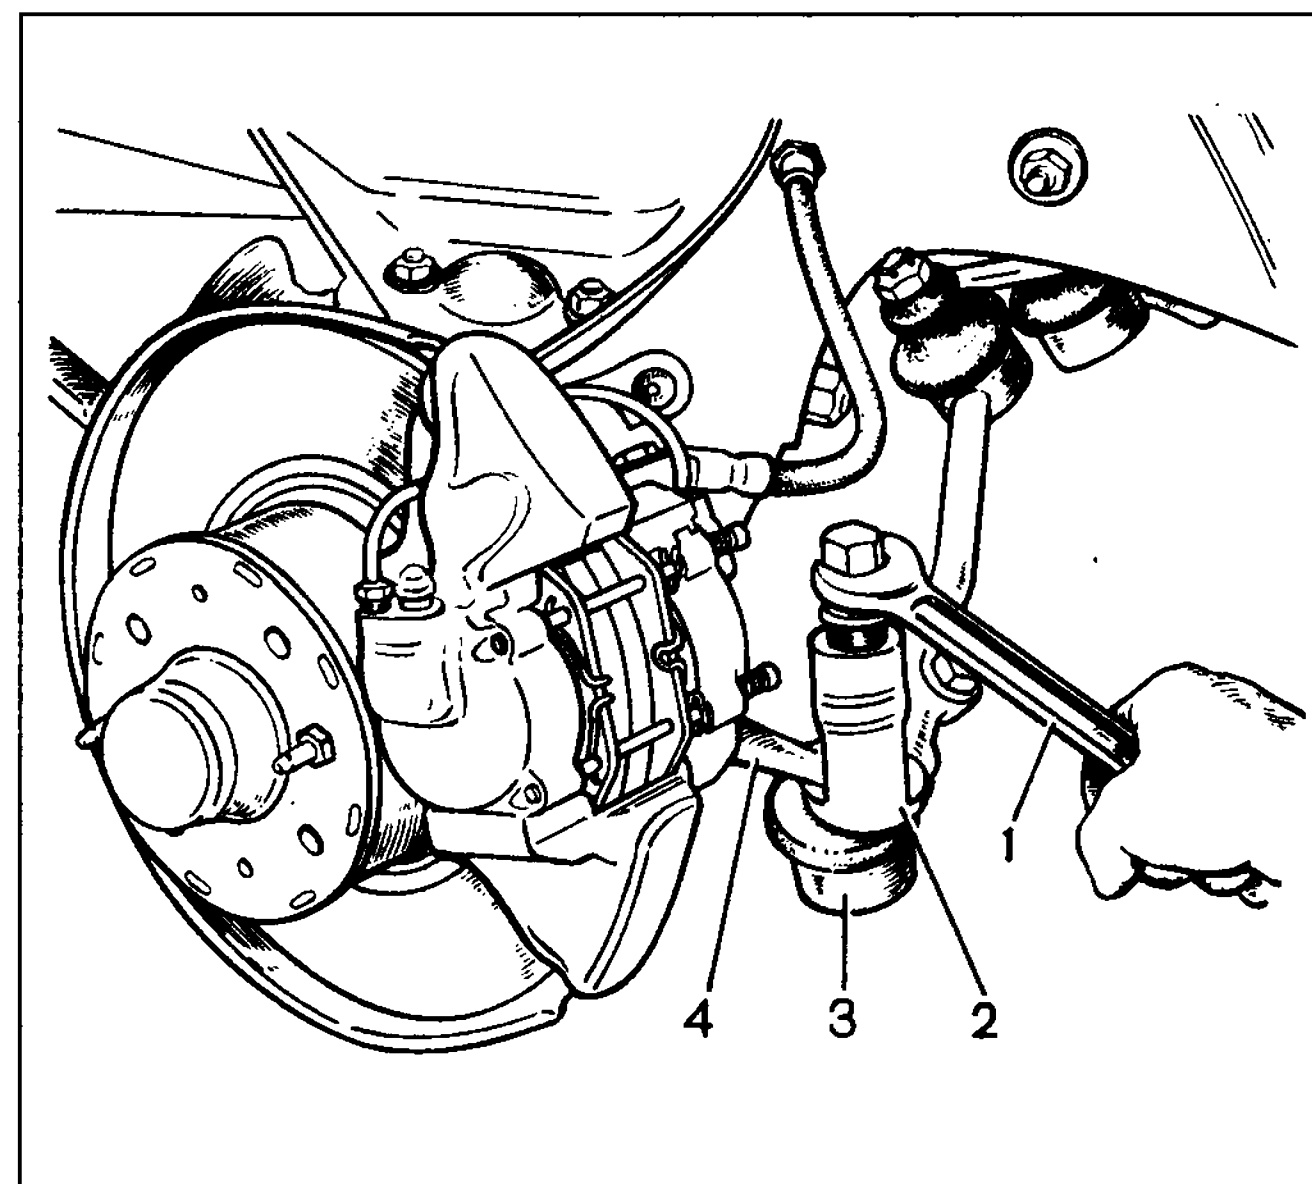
Снятие шаровых пальцев тяг рулевой трапеции: 1-ключ гаечный; 2-съемник А.47052; 3-шаровой шарнир; 4-рычаг поворотного кулака
